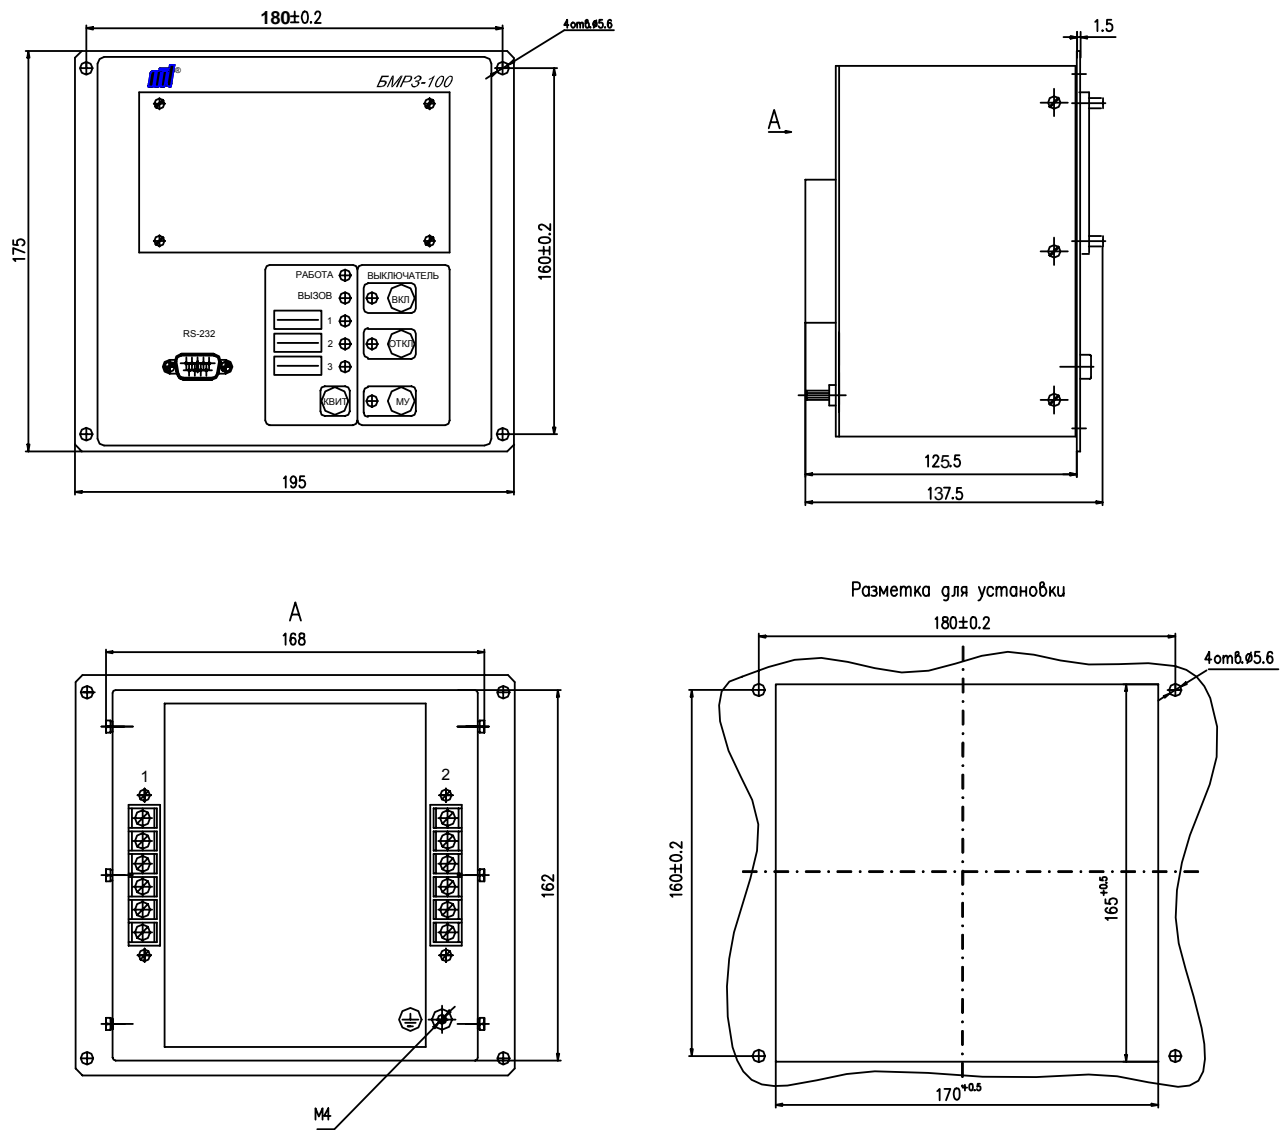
Габаритные и установочные размеры BMP3-100
